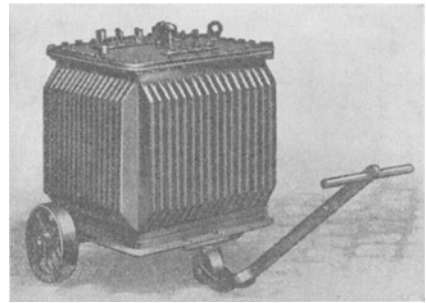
Fahrbarer Schweißtransformator mit Ölkühlung.
